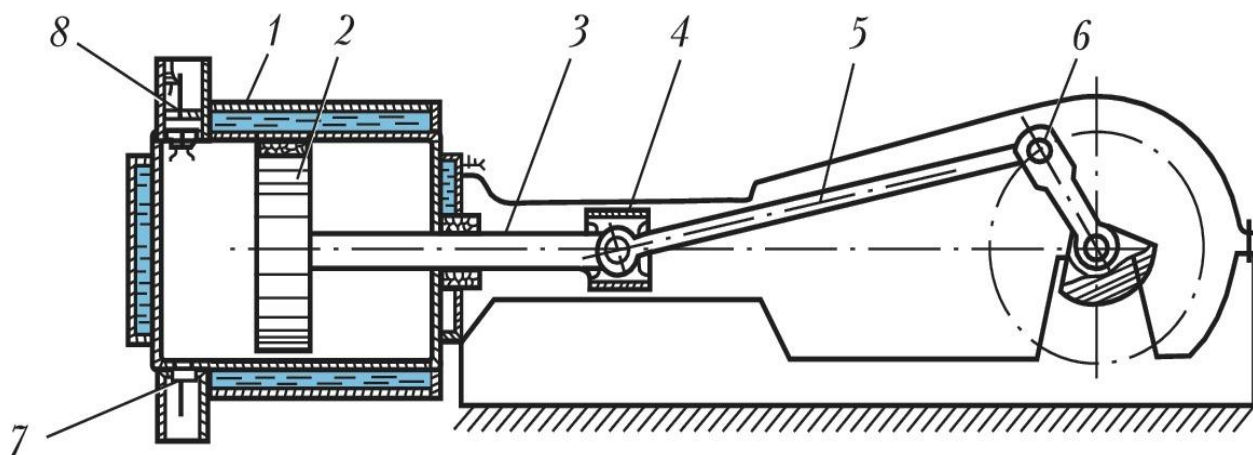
Одноступенчатый поршневой компрессор крейцкопфного типа: 1 – цилиндр; 2 – поршень; 3 – шток; 4 – крейцкопф; 5 – шатун; 6 – кривошип; 7 и 8 – всасывающий и нагнетательный клапаны
